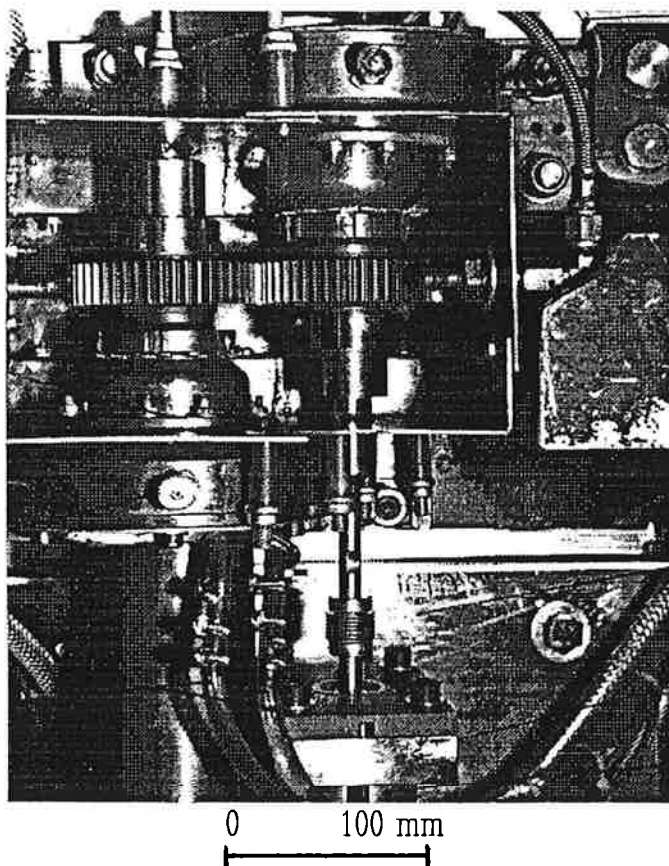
Photographie du détail du montage des engrenages et du boîtier.
